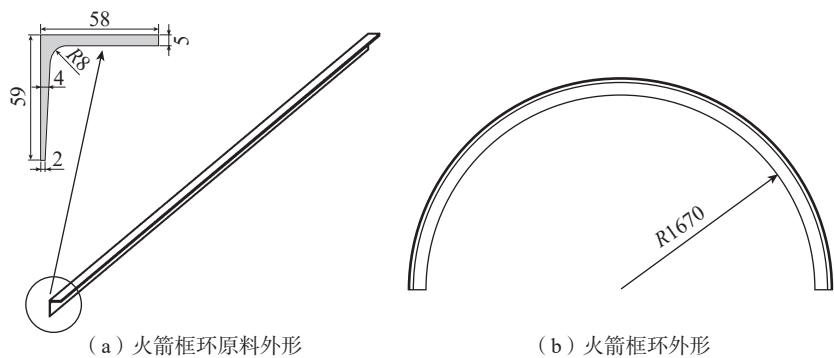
火箭框环的原料尺寸和设计尺寸 (mm)
